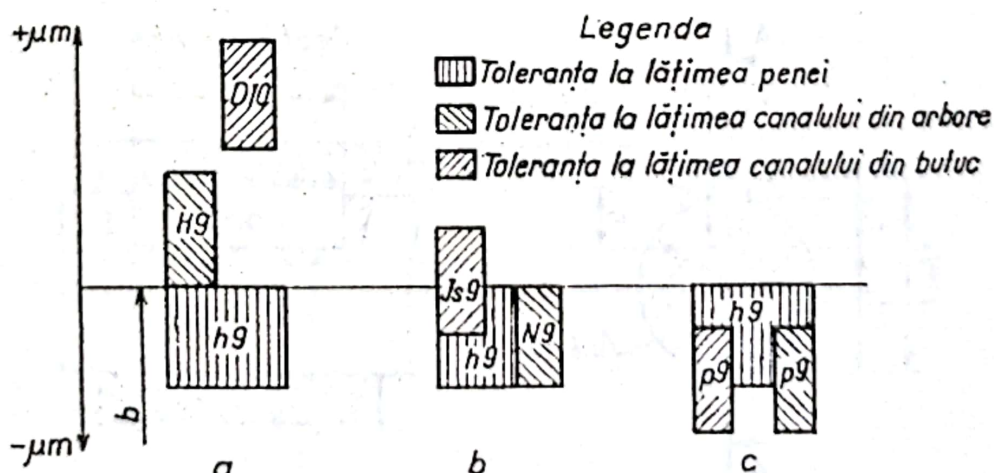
Ajustaje pentru asamblările butuc-pană paralelă-arbore.
